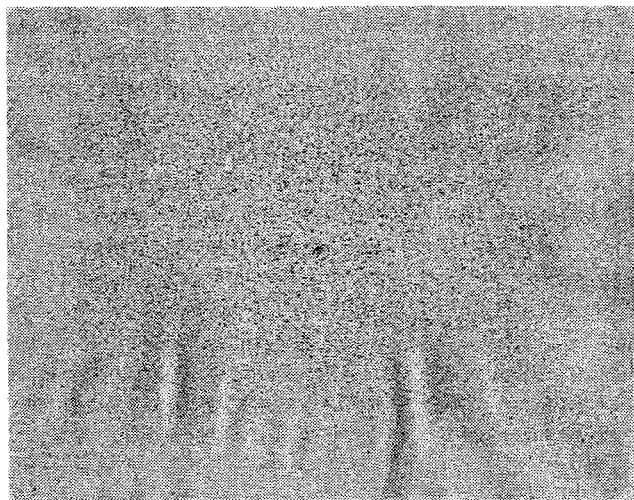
Макроструктура литой заготовки плавки №35529 2-2
